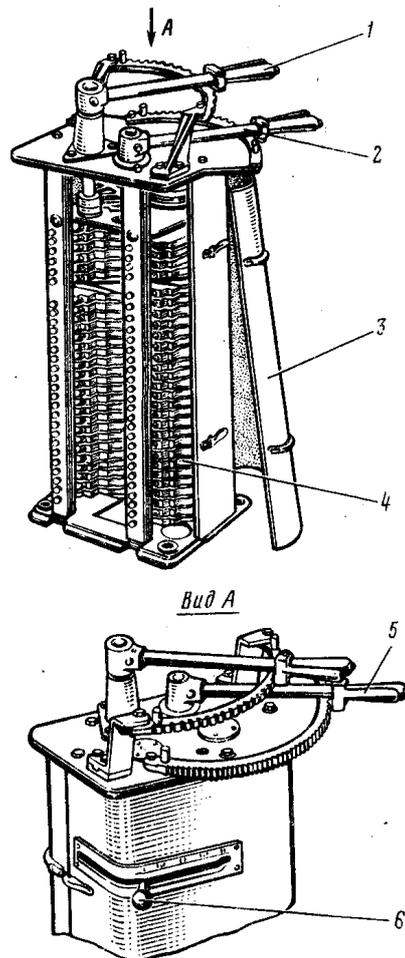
Контроллер машиниста электровоза с индивидуальными контакторами: 1 – тормозная рукоятка; 2 – главная рукоятка; 3 – кожух; 4 – главный вал с контактами; 5 – фиксатор; 6 – реверсивно-селективная рукоятка
